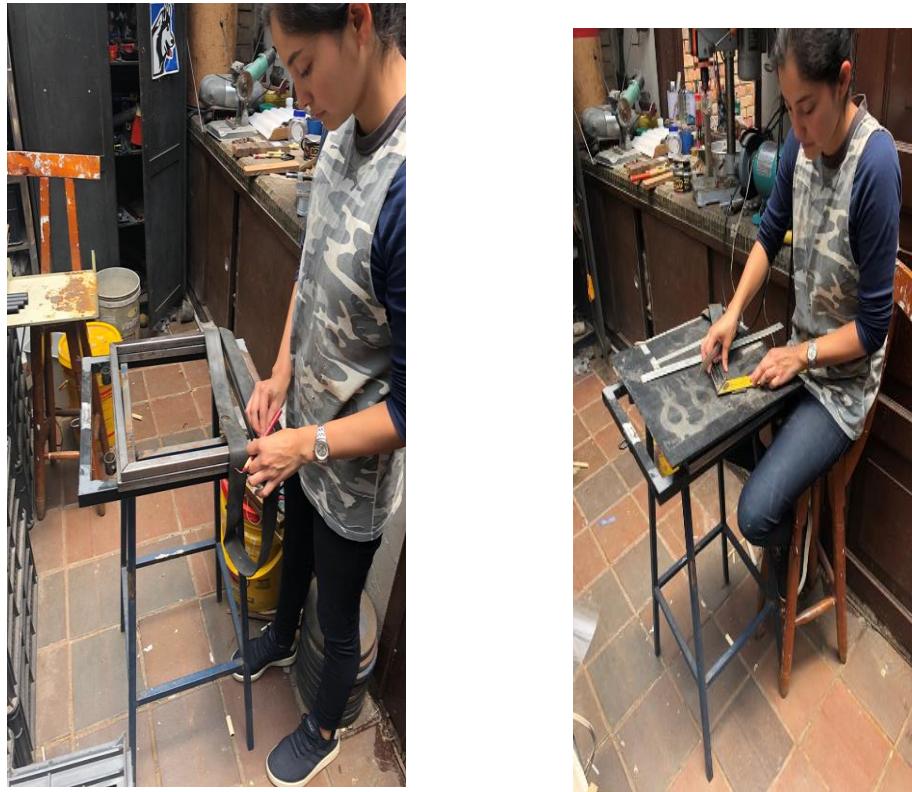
Soldadura del seguro con arco eléctrico. Fuente: Autores.
